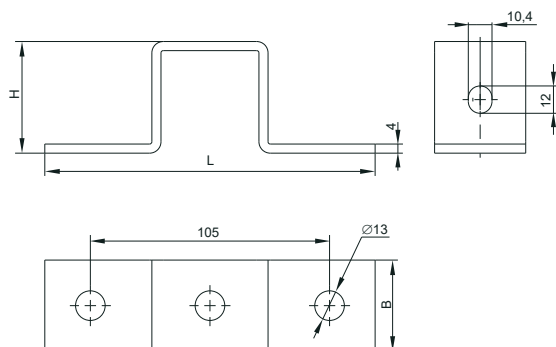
Крепление стеновое для STRUT-профиля / Figure C.1 – Wall attachment for STRUT profile
